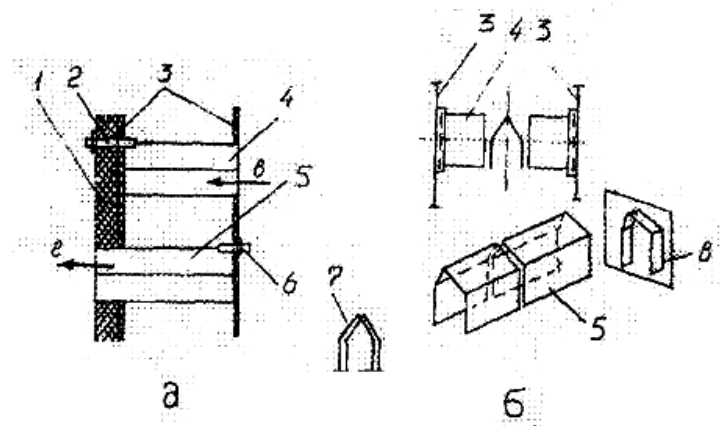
Установка коробов в шахте зерносушилки:
